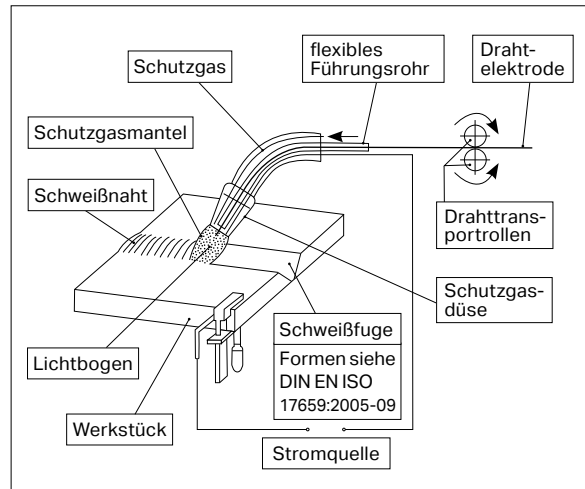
Prinzip des Metallschutzgasschweißens⁽⁹⁾
